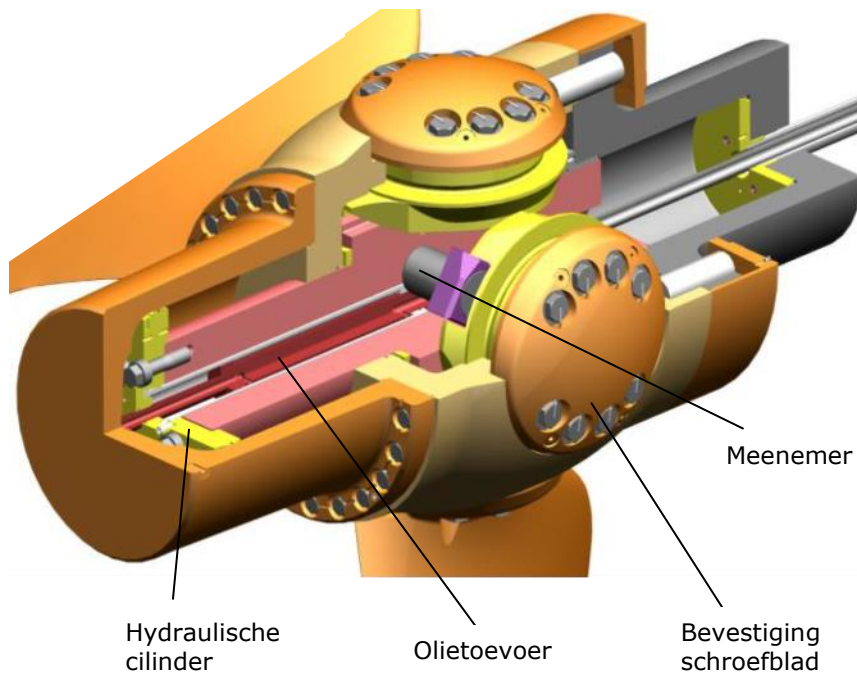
Verstelbare schroef. Bron: Wärtsilä.
